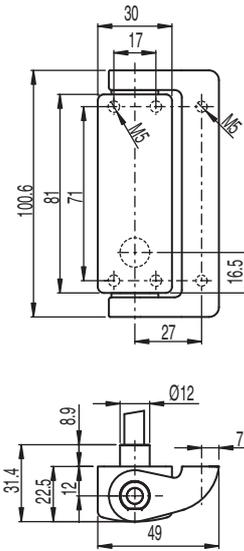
Dimensioni dell'S400-M4-CB2PUR-W in mm
